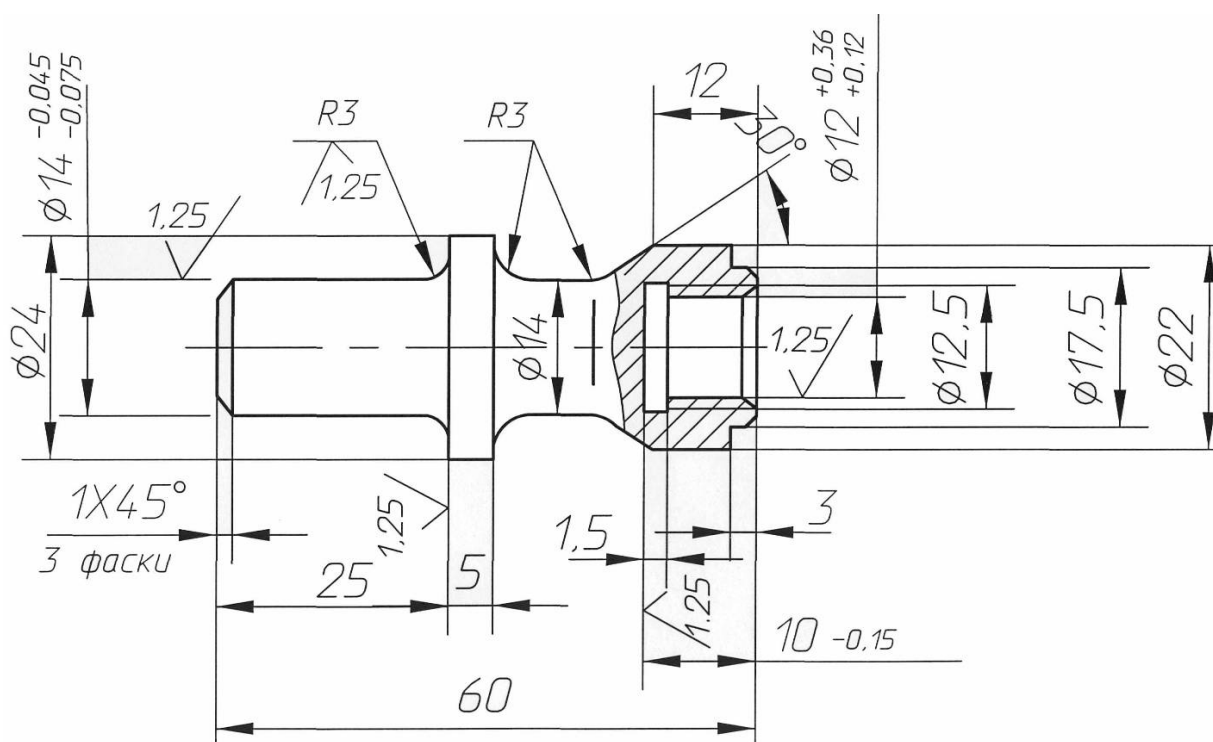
Оправка для запрессовки передней втулки оси толкателей в отверстие переднего торца блока цилиндров
